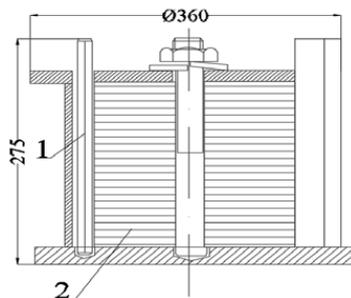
Схема термофиксатора: 1 – фиксатор; 2 – косорасположенное прорезью кольцо
